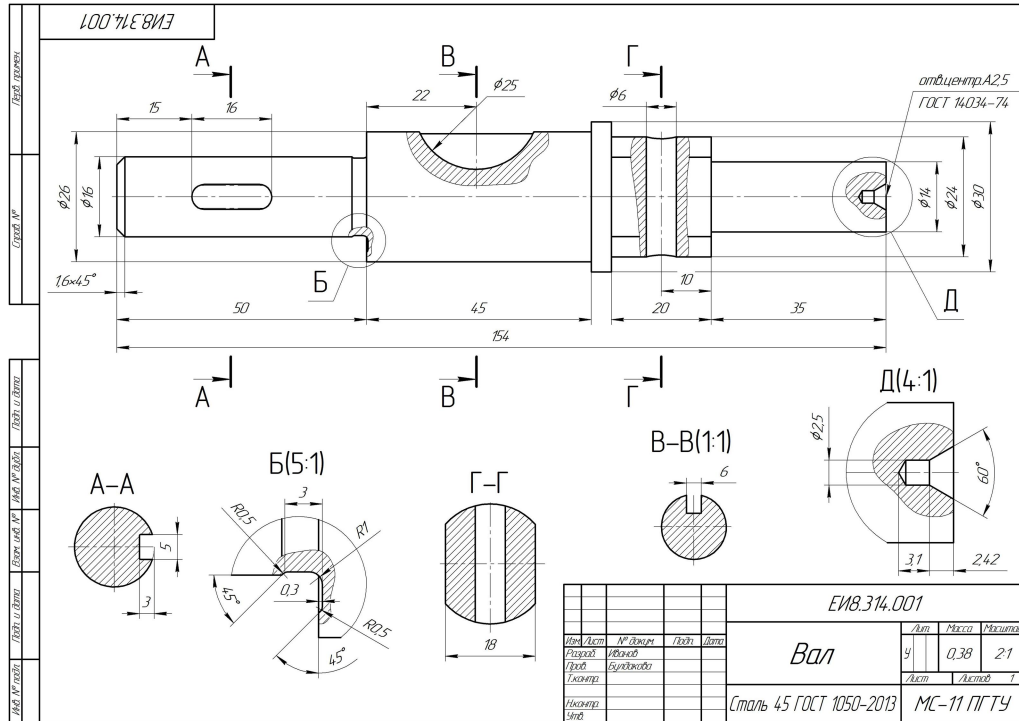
Ассоциативный чертеж вала в КОМПАС-3D
